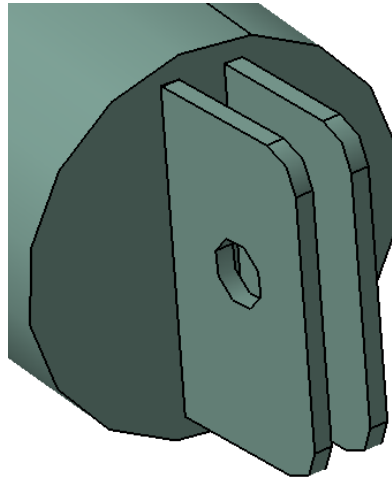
Seat mounting frame 11*: Elementos soldados en la barra diagonal
